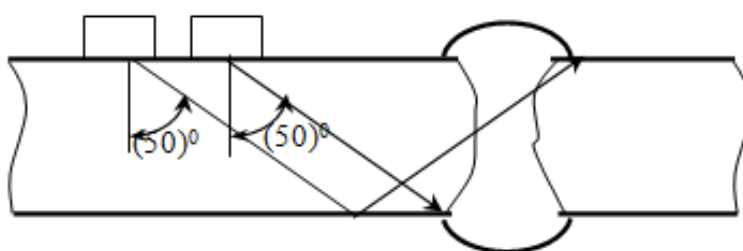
Испытание зоны сварного шва с углом  $50^\circ$
